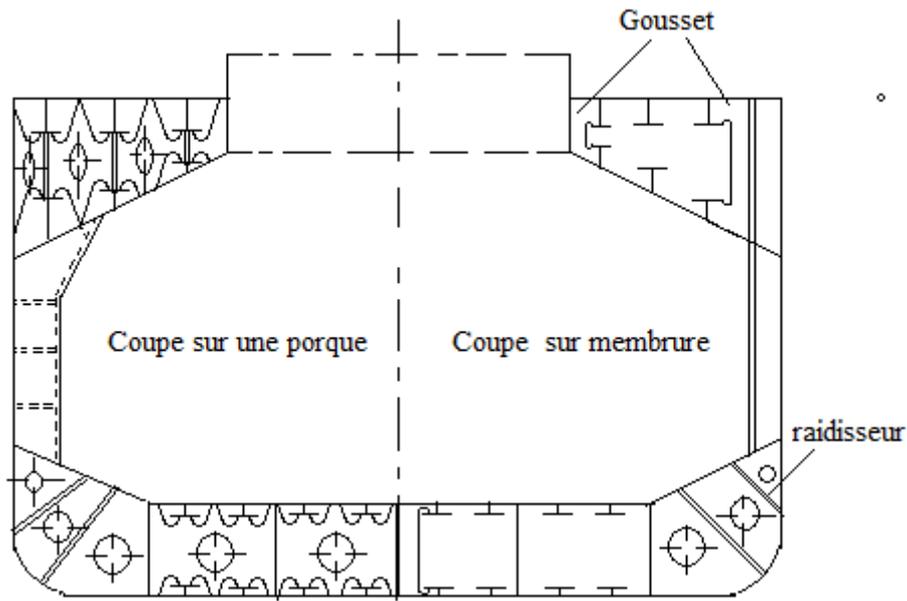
Construction longitudinale du bordé de la muraille des vraquiers.
